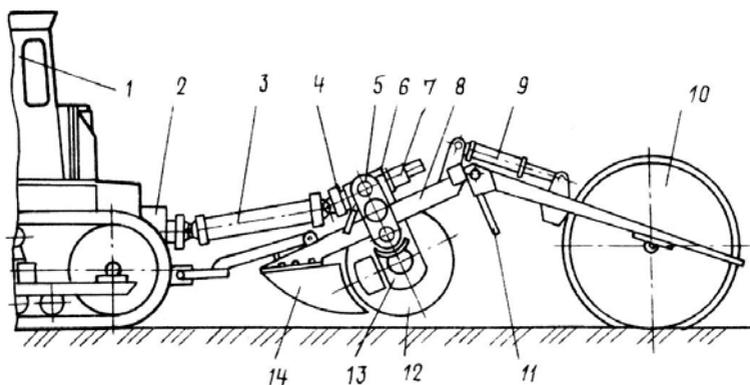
Машина для фрезерования земель МТП-44А: 1 – трактор базовый; 2 – ходоуменьшитель; 3 – карданная передача; 4 – демпфер; 5 – редуктор бортовой; 6 – редуктор конический; 7 – муфта фрикционная; 8 – рама; 9 – гидроцилиндр; 10 – каток задний; 11 – гребенка сепараторная; 12 – фреза; 13 – редуктор фрезы; 14 – плита отбойная
